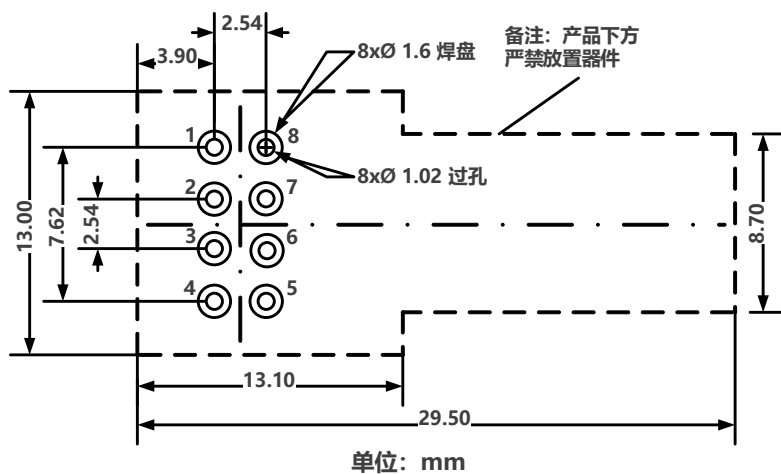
PCB Layout 设计推荐尺寸图 (俯视图)
